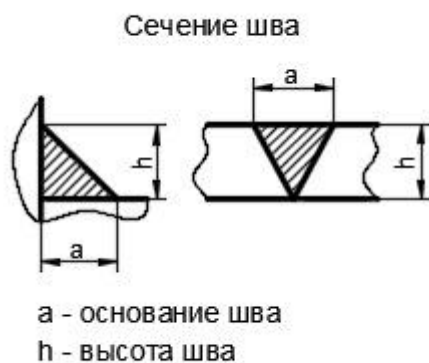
Площадь сечения сварочного шва.
